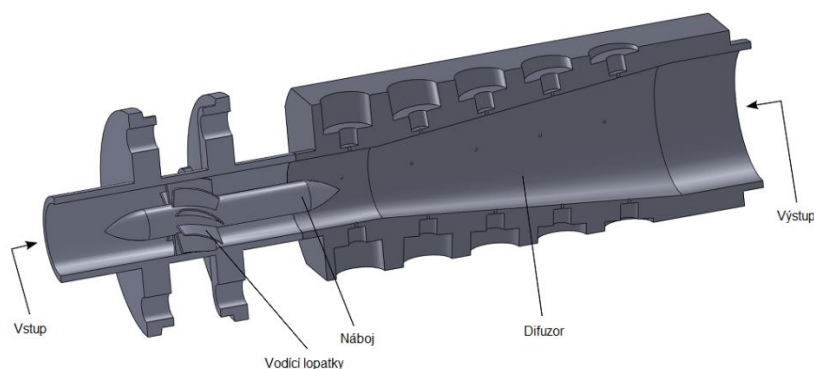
Vírový generátor Stuttgart, upraveno a převzato z [24]
